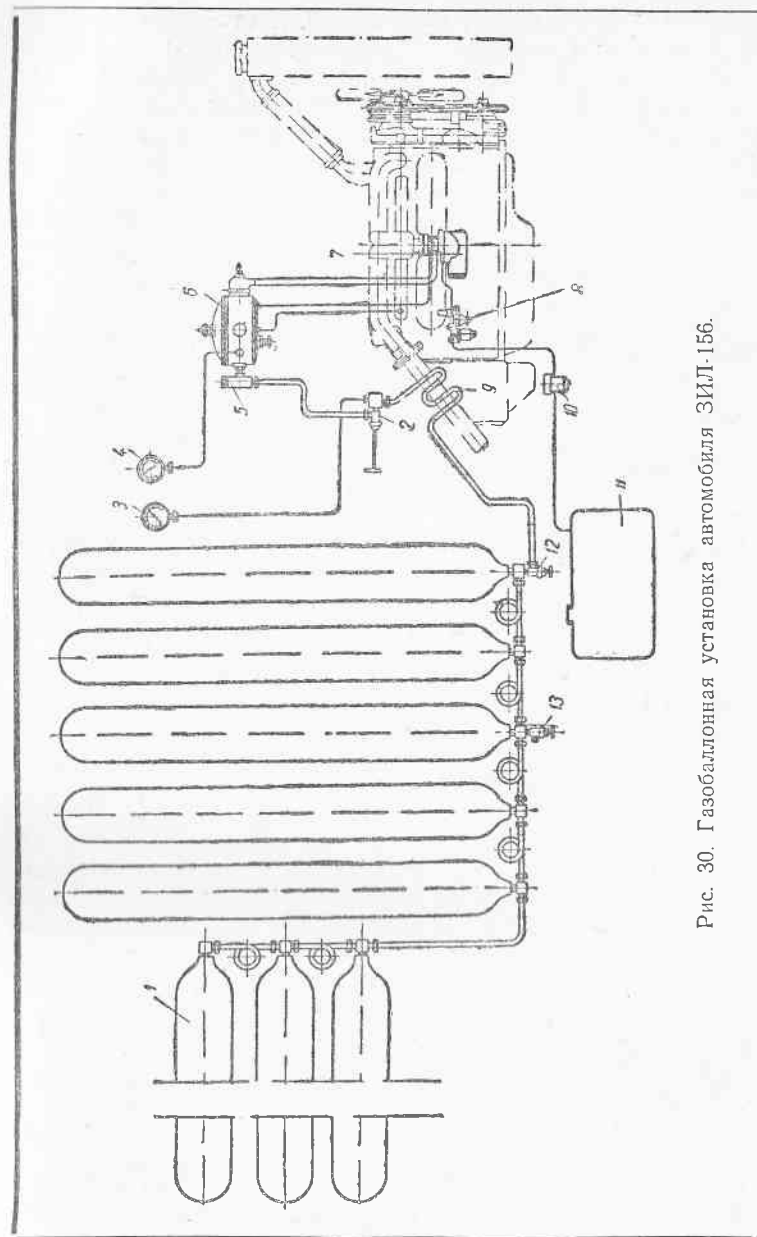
Газобаллонная установка автомобиля ЗИЛ-156.
